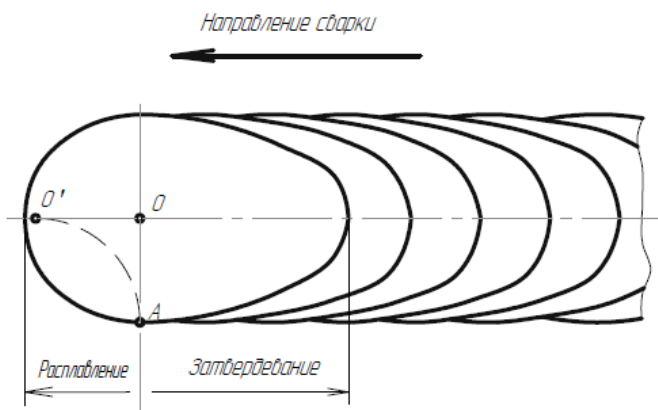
Схема роста кристаллита в движущейся сварочной ванне (штриховая линия — ось растущего кристаллита)
